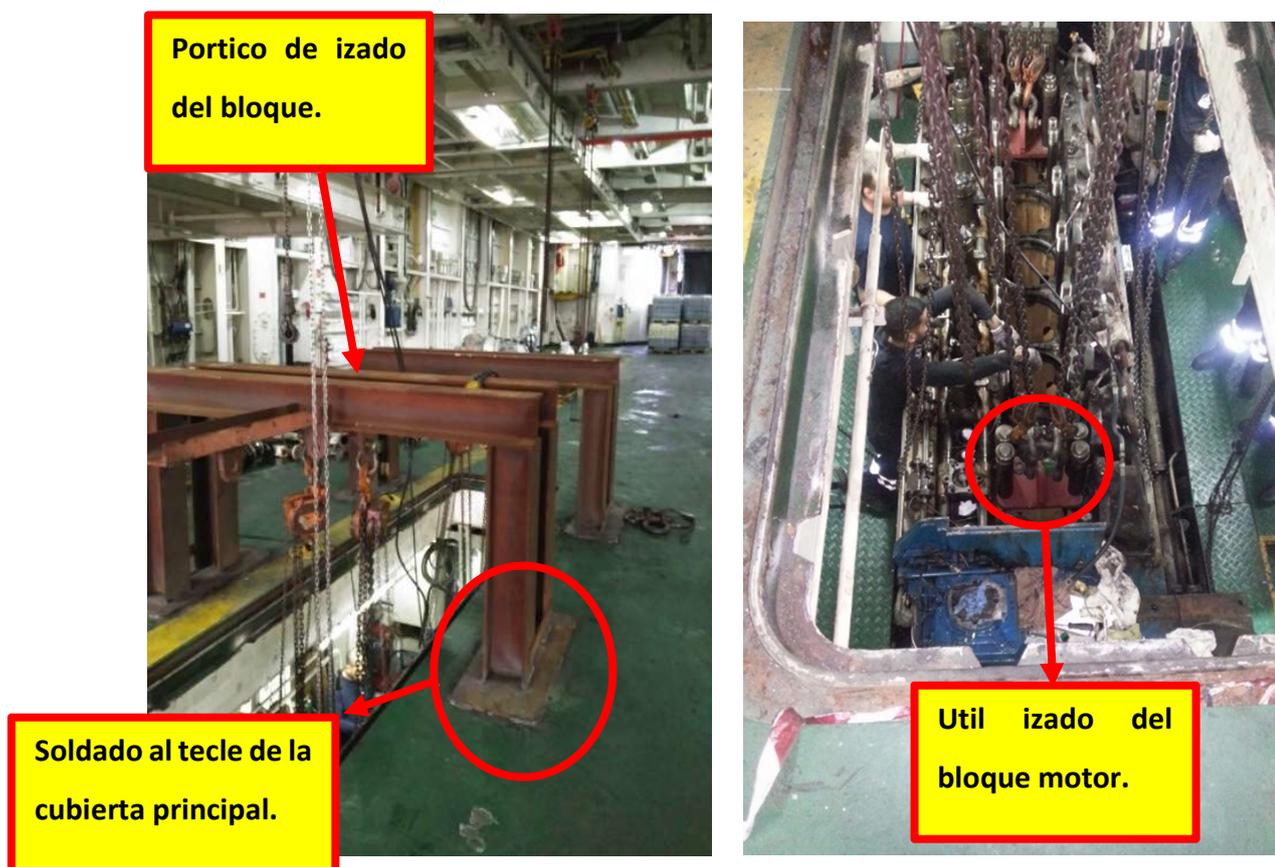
Detalle de la maniobra de izado del bloque. Fuente: Trabajo de campo.
